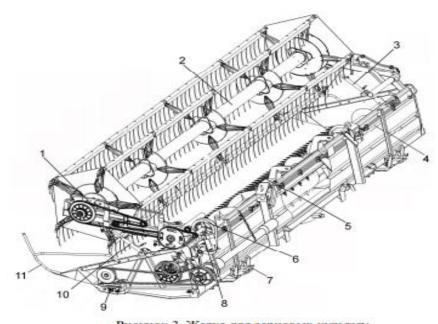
Жатка для зерновых культур: 1 — гидроцилиндр выноса мотовила; 2 — мотовило; 3, 10 — гидроцилиндры подъема мотовила по высоте; 4 — рама жатки; 5 — режущий аппарат; 6 — вариатор; 7 — копирующий башмак; 8 — исполнительный электромеханизм; 9 — угловая передача; 11 — прутковый делитель.
